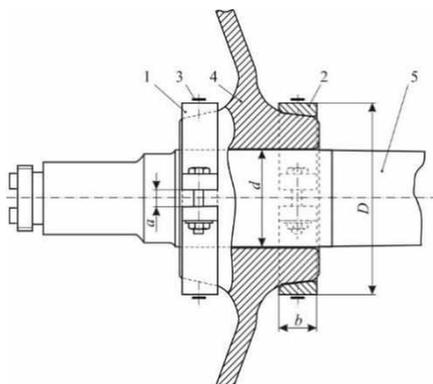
Устройство для контроля прочности механической напрессовки колеса на ось колёсной пары:
